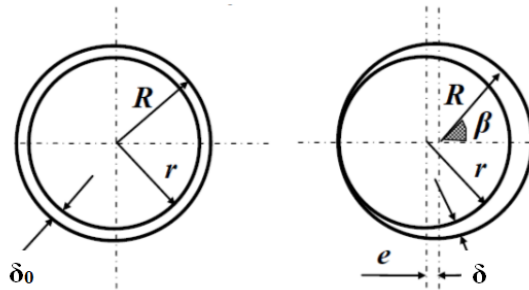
Расположение поверхностей раздела образующих кольцевой зазор в сопряжении «плунжер - втулка»
